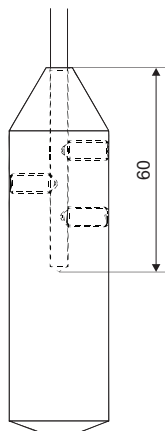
Zobrazení závitového spoje držáku elektrody s tyčovou elektrodou
